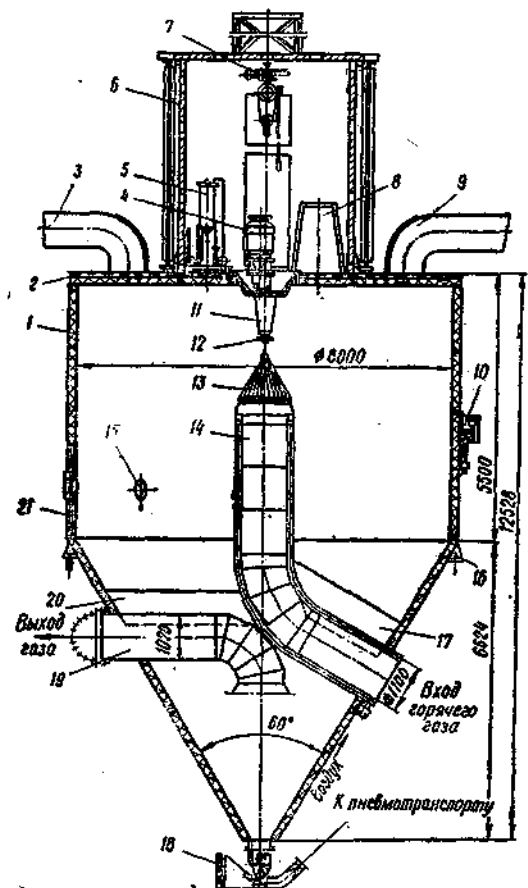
Распылительная сушилка СРЦ-1600: 1 — корпус сушильной камеры; 3 — перекрытие камеры; 3, 9 — штурупы предохранительных клапанов; 4 — электродвигатель; 5 — масляный фильтр; 6 — шатер; 7 — электроваль; 8 — подставка; 10 — вибратор; 11 — центробежный распыляющий механизм; 12 — распыляющий диск; 13 — захлывающаяся головка; 14 — трубопровод для сушильного агента; 15 — окно; 16 — опора сушильной камеры; 17, 20 — защитные козырьки; 18 — выгрузчик к пневмотранспорту; 19 — трубопровод отработанного агента; 21 — дверь
